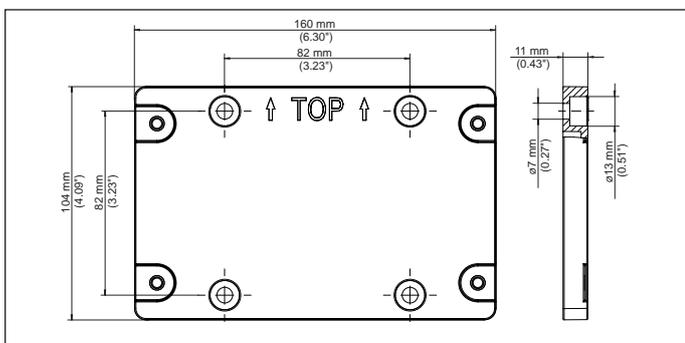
Dimensiones placa de montaje VEGAMET 841, 842
